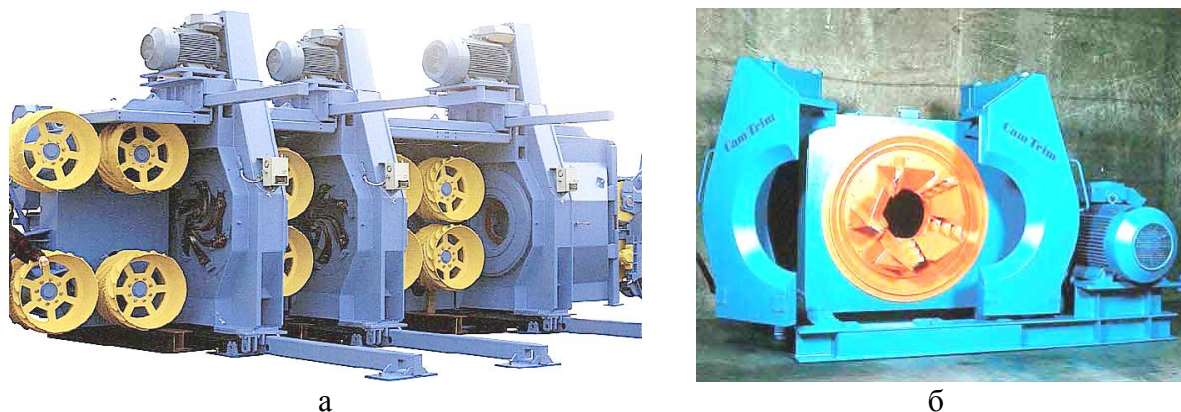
Многороторные станки: а – трехроторный окорочно-оцилиндровочный станок VK-COMBI-3R [10]; б – ротор оцилиндровочного станка Cambio [21]
